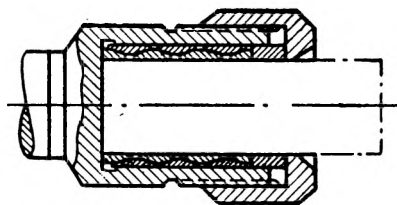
Цанговый патрон с кольцевыми пружинящими уплотнителями.
